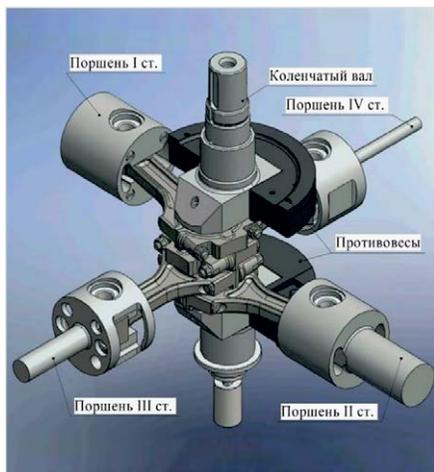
Механизм движения четырехрядного компрессора с вертикальным коленчатым валом
